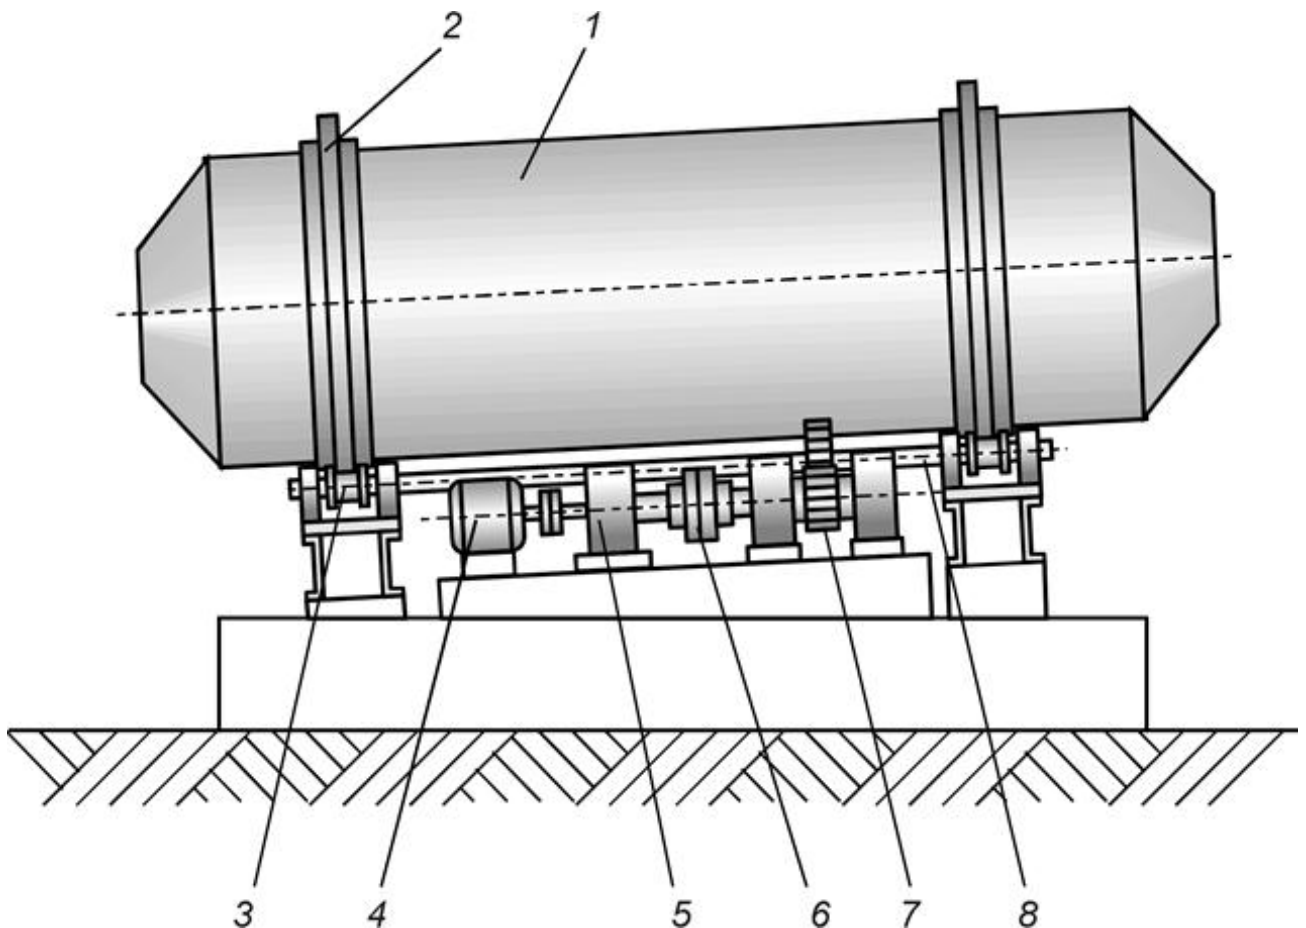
Галтовочный барабан непрерывного действия
